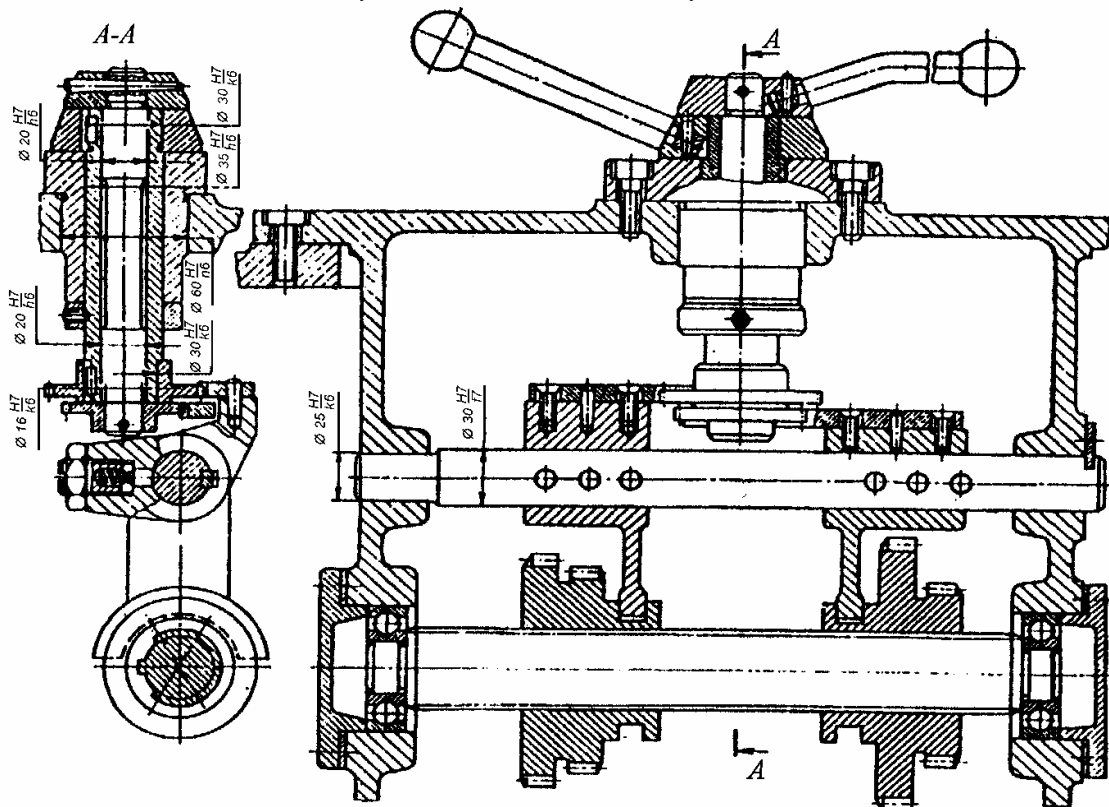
Управление двумя блоками зубчатых колес посредством ползун-вилок, зубчато-реечного механизма и двух соосных рукояток
